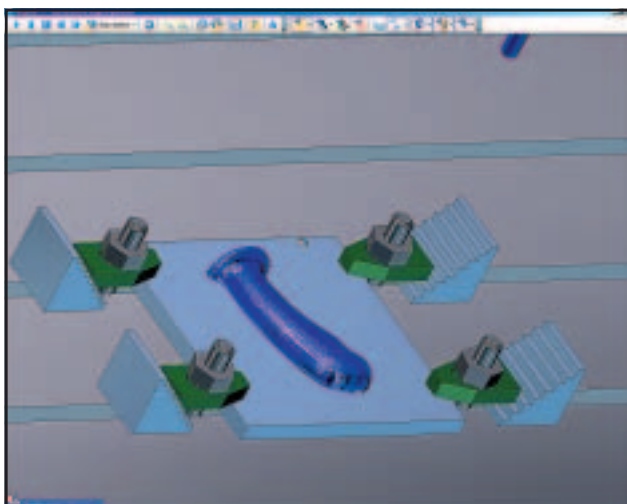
Обработка одной из частей ручки джойстика по 3D-модели в Pathtrace EdgeCAM
